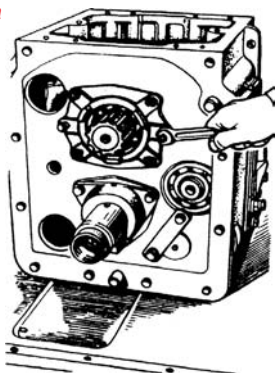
Снятие стопорного кольца подшипника первичного вала.
